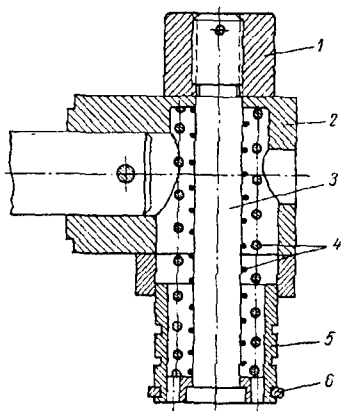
Конструкция вибратора с выдвигным дебалансом:
